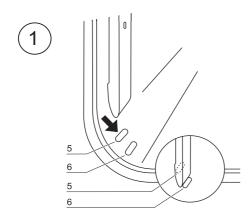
Монтаж и демонтаж креплений и полок
